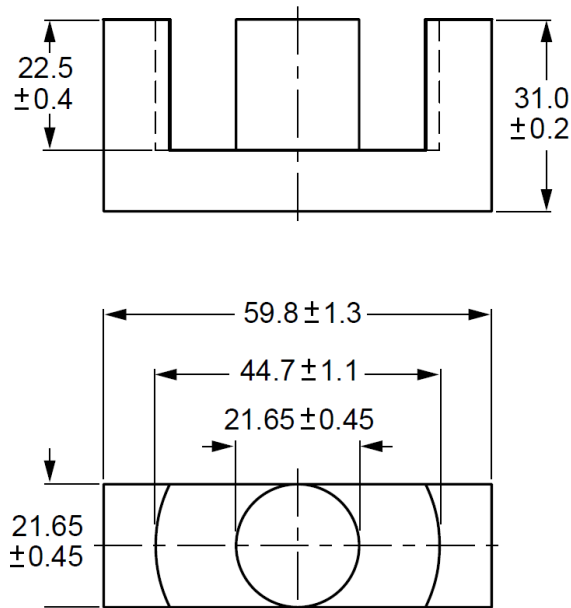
Dimensions du noyau magnétique en ferrite (en mm)
